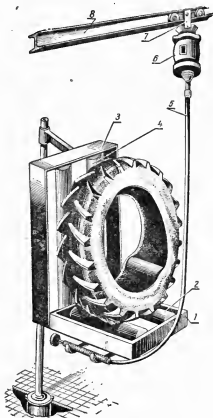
Внутренняя шероховка покрышки на пневматическом подъемнике:
